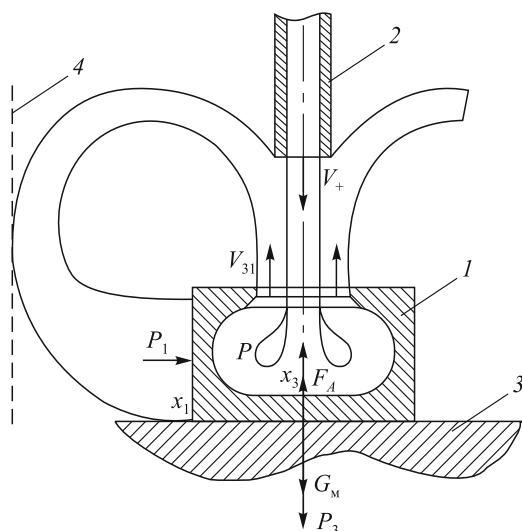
Компоновка металлоприемника в ПК: 1 – металлоприемник; 2 – приемная труба; 3 – дно ПК; 4 – стенка ПК
